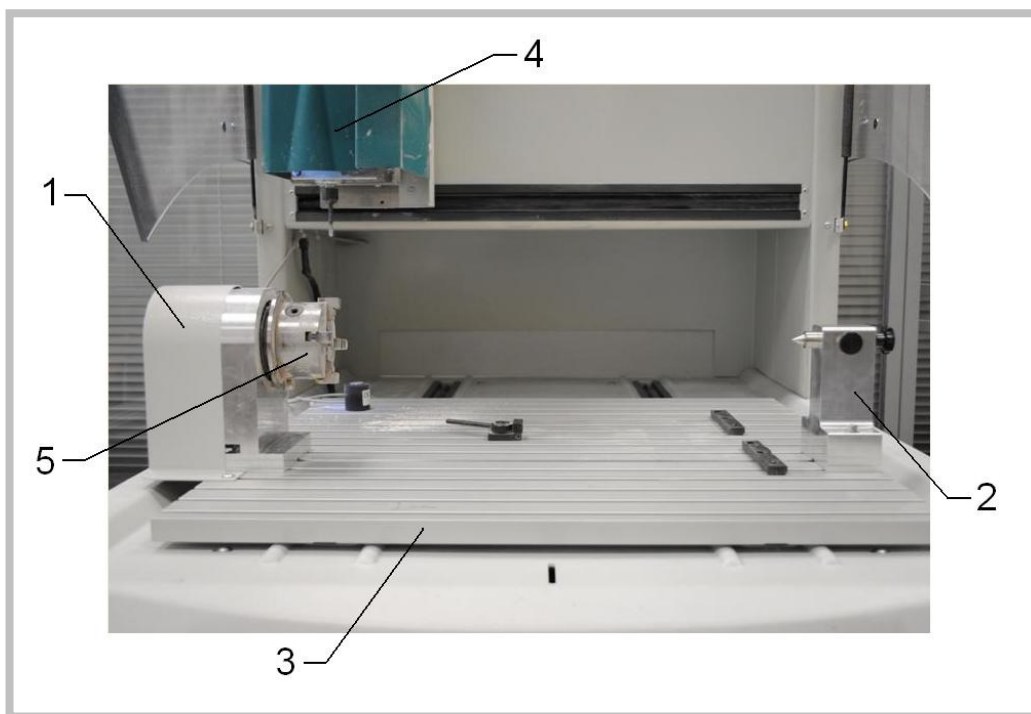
Otočný stůl s motorem na svislo Hass HRT210M.
